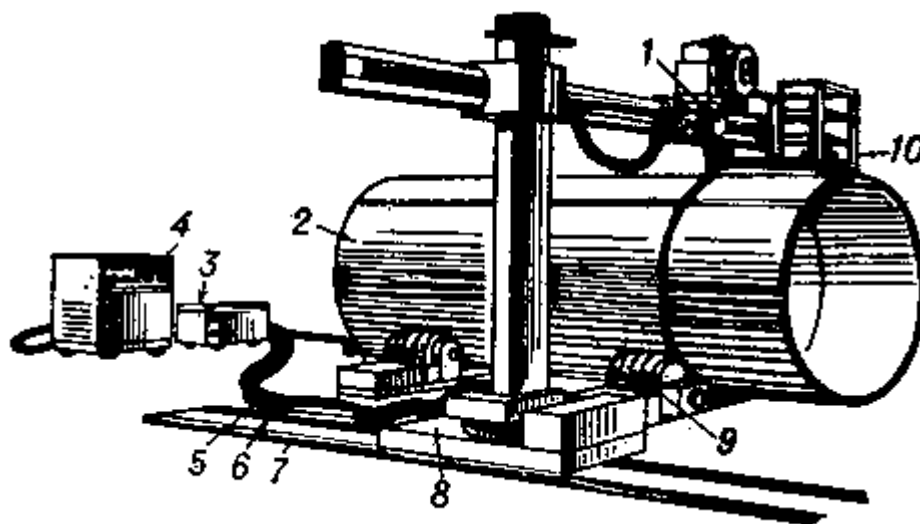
Установка для дуговой автоматической сварки
